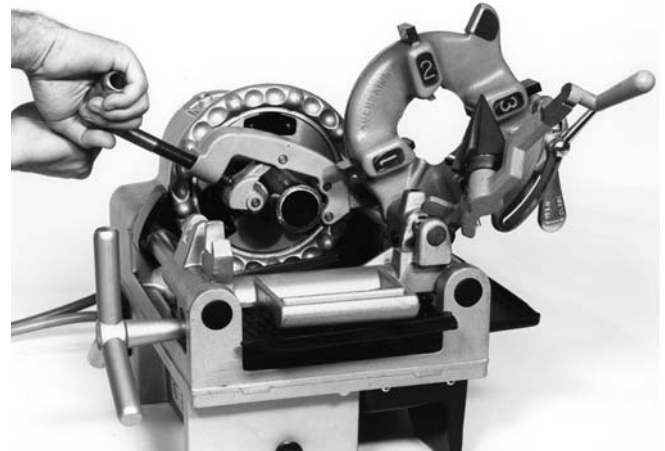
Corte de un tubo con el Cortatubos No. 732
